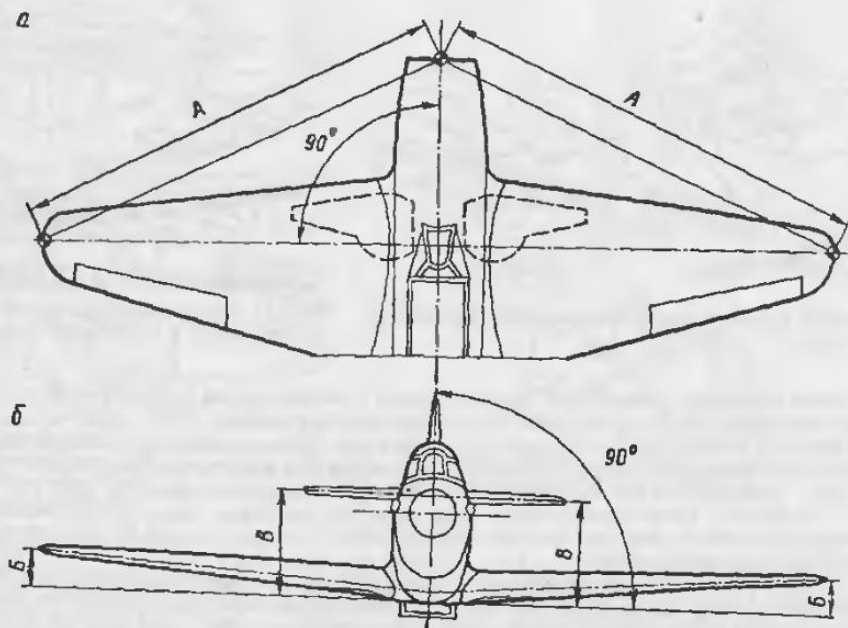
Способ проверки правильности установки агрегатов модели самолета в процессе общей сборки: а - вид в плане; б - вид спереди
